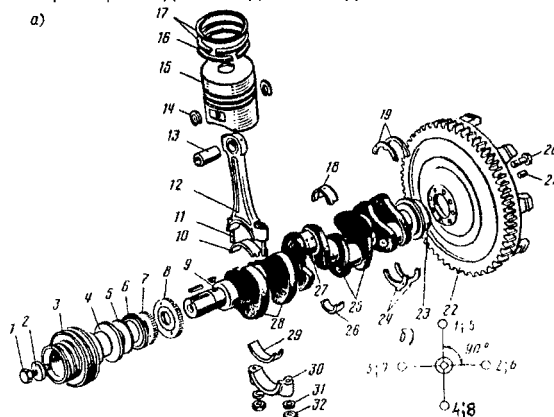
Кривошипно-шатунный механизм двигателя ЗИЛ-130:
